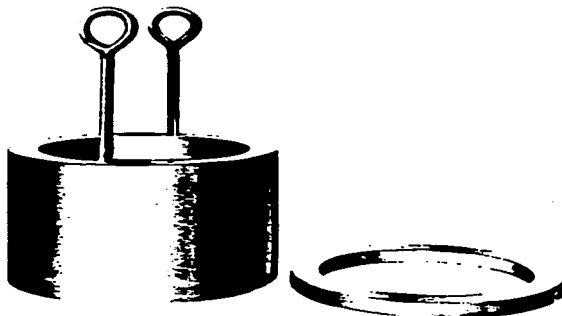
ROLDANA DE DESGASTE Y MANGUITO DE LA FLECHA PRINCIPAL
